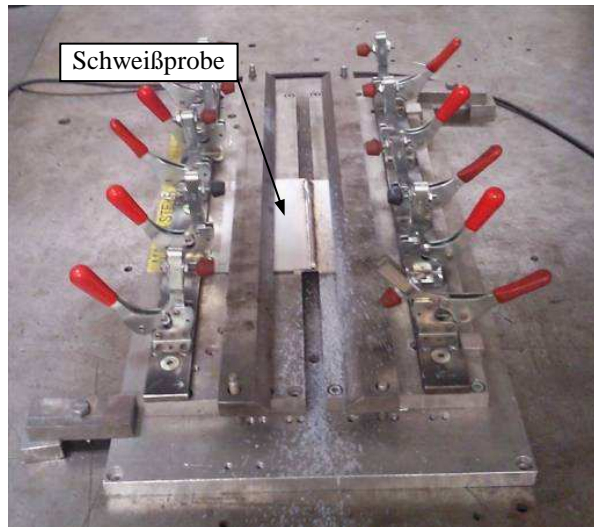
Spannvorrichtung zum Schweißen
